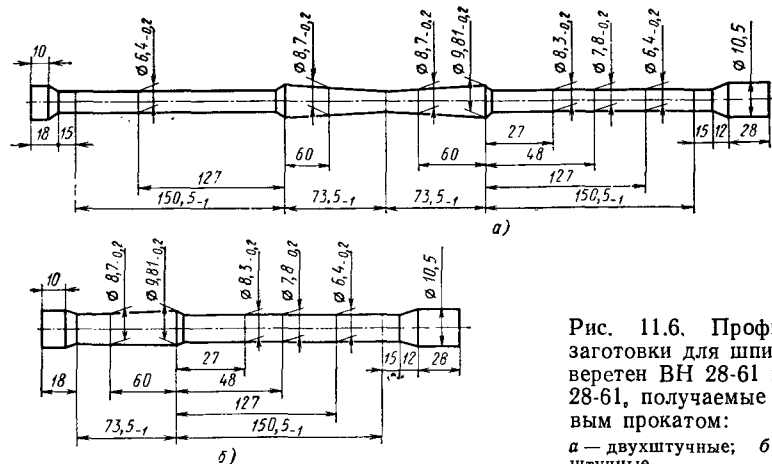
Профильные заготовки для шпинделей веретен ВН 28-61 и ВНТ 28-61, получаемые винтовым прокатом:
